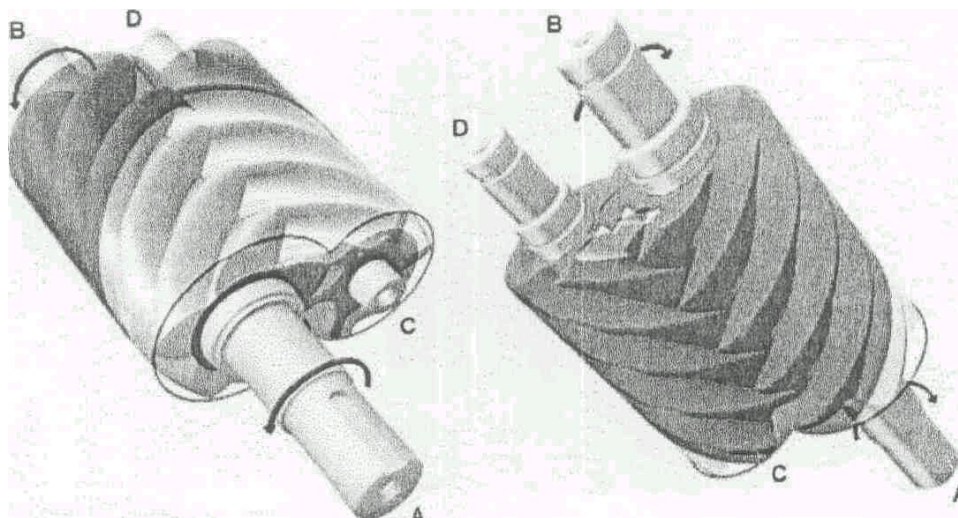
Форма рабочих камер винтового компрессора
